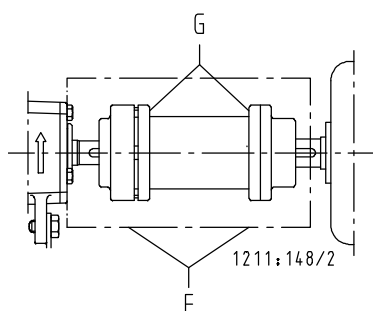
Места затяжки резьбовых соединений муфты с проставком
